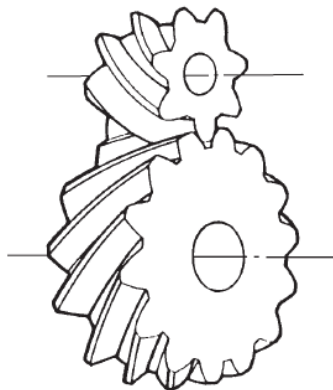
Engrenagem cilíndrica de dentado helicoidal
